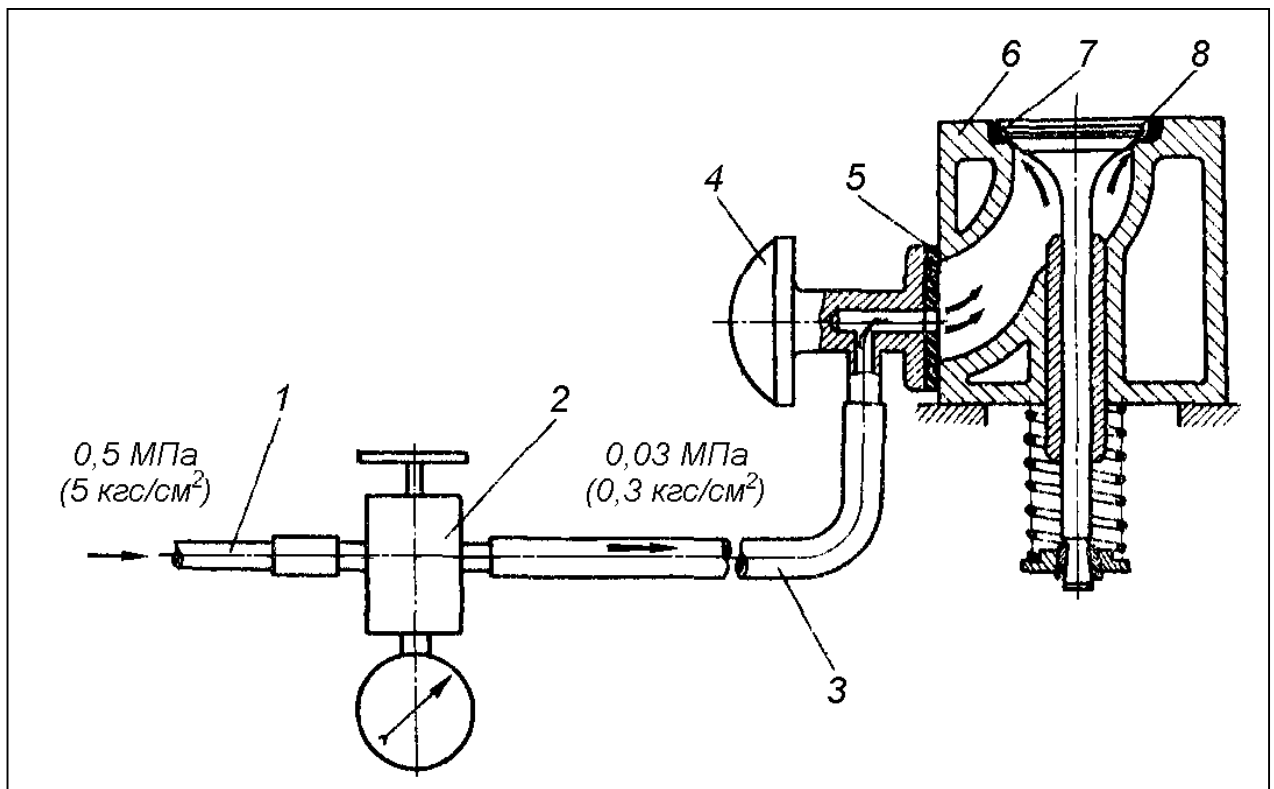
Схема действия пневматического приспособления при проверке герметичности клапанов: 1 – воздушная магистраль; 2 – воздушный редуктор и манометр; 3 – шланг; 4 – корпус прижимной; 5 – прокладка уплотнительная; 6 – головка цилиндра; 7 – дизельное топливо; 8 – воздушные пузыри.
